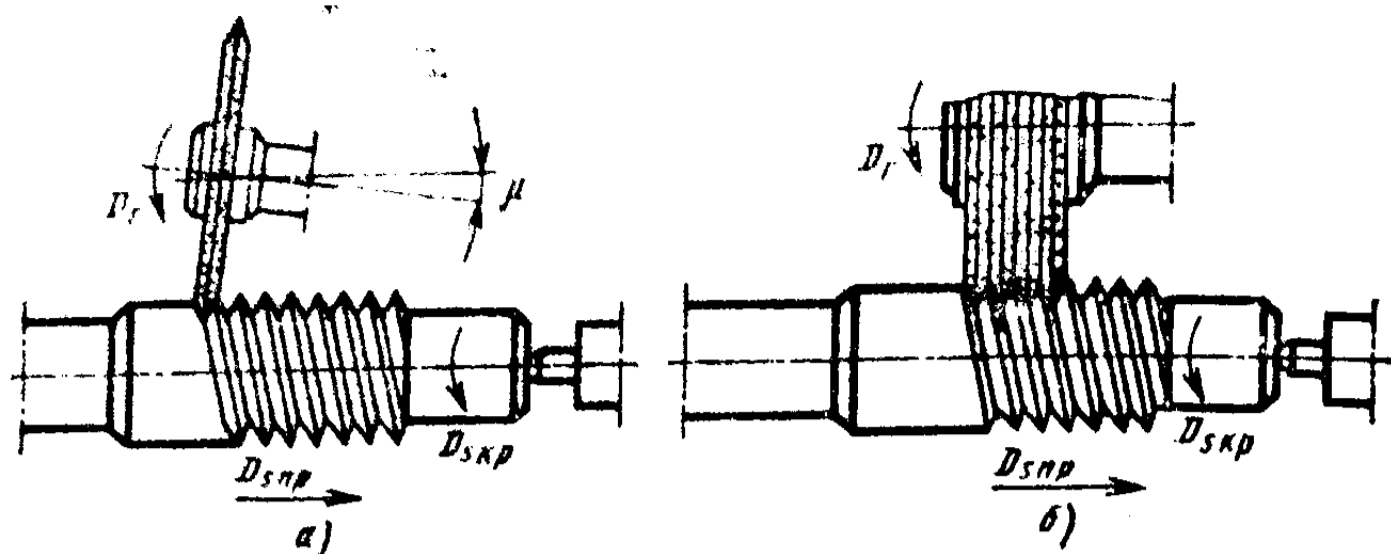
Схемы нарезания резьб на резьбошлифовальном станке кругом:
